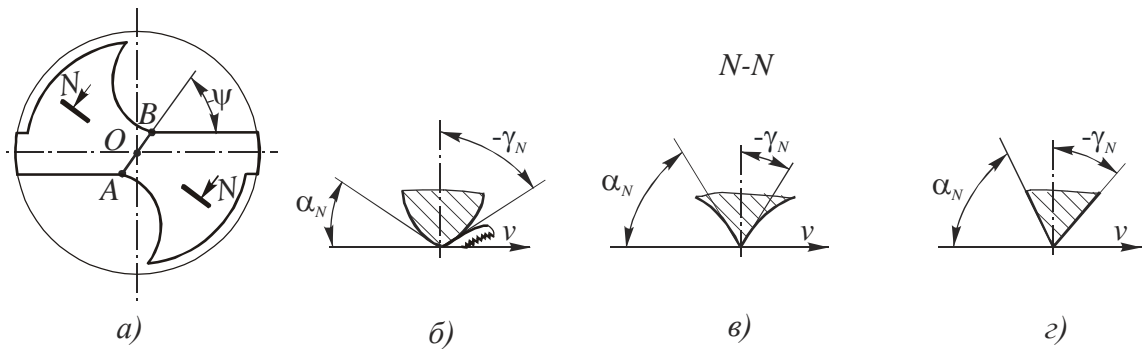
Передние углы на поперечной режущей кромке спирального сверла:
